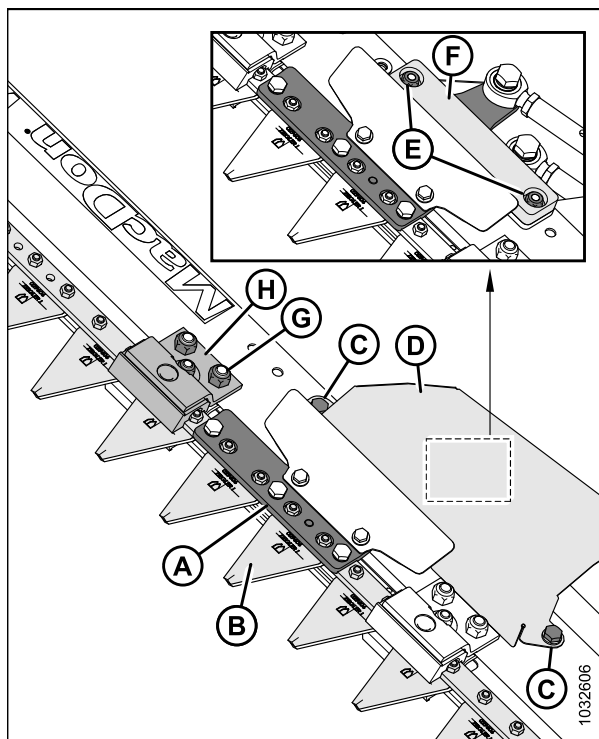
Вертикальный нож — противорежущий палец снят
